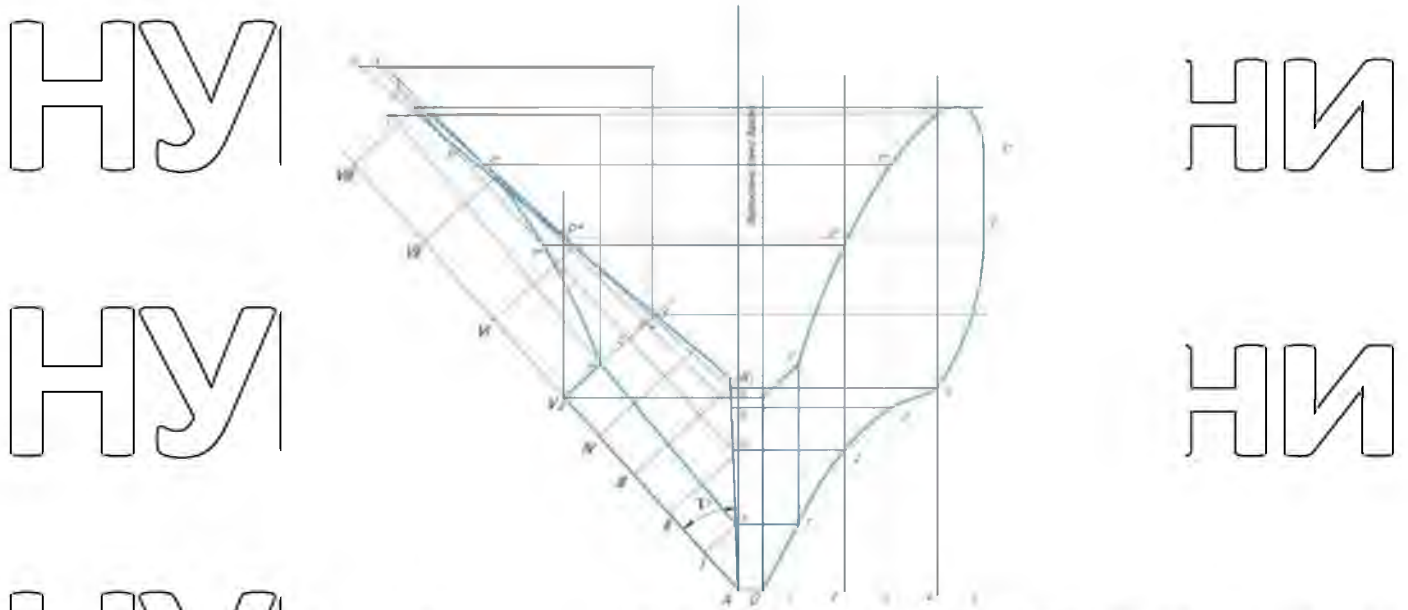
Побудова горизонтальної і бокової проєкції робочої циліндроїдальної поверхні корпусу
